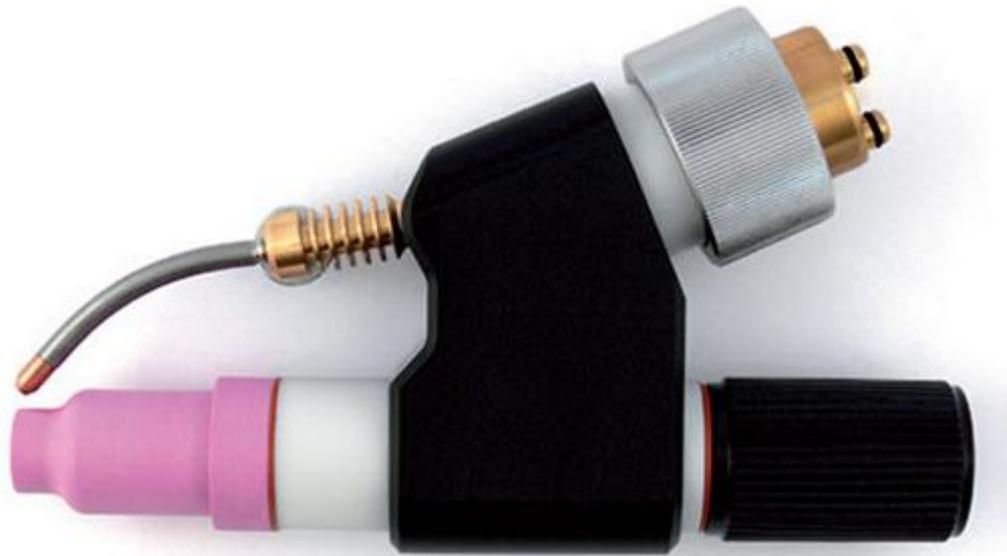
Головка сварочная RT TIG
